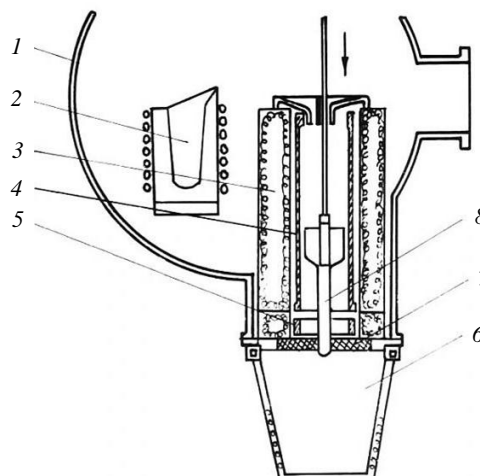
Принципиальная схема конструкции установки УВНЭС-3 с жидкометаллическим охладителем: 1 – вакуумная камера; 2 – плавильный тигель; 3 – печь подогрева форм; 4 – верхний нагреватель; 5 – нижний нагреватель; 6 – ванна с расплавленным оловом; 7 – тепловой экран; 8 – керамическая форма
